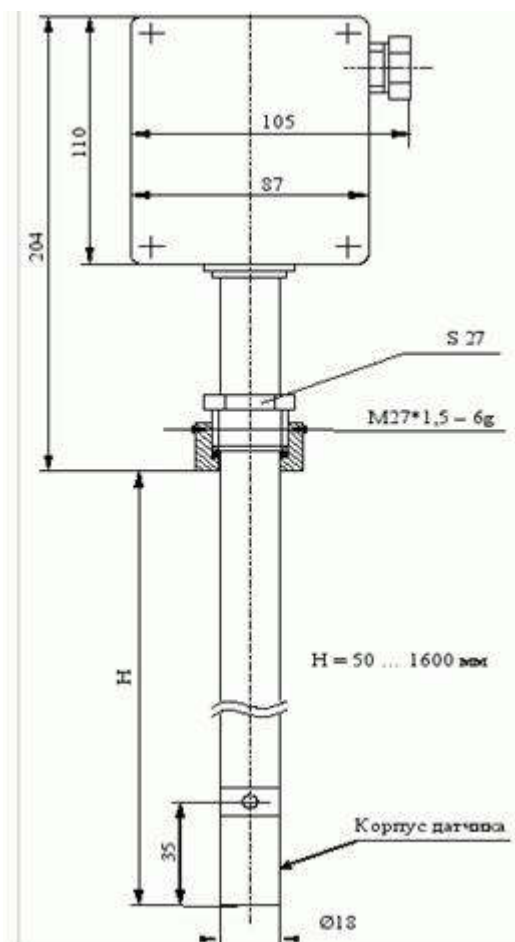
Первичный преобразователь с корпусом из дюралюминия, тип, погружной, с бобышкой под приварку
